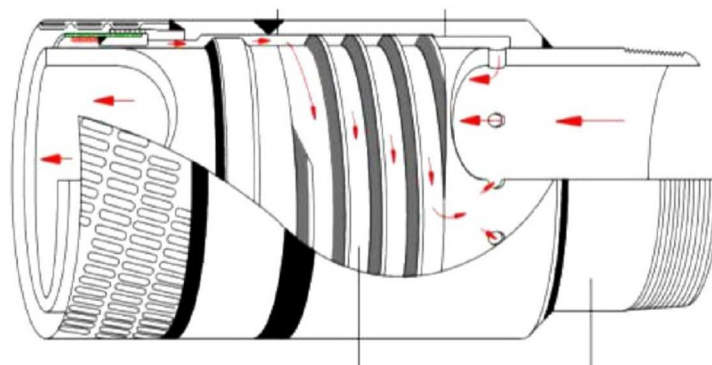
Устройство контроля притока («Baker Hughes»)
